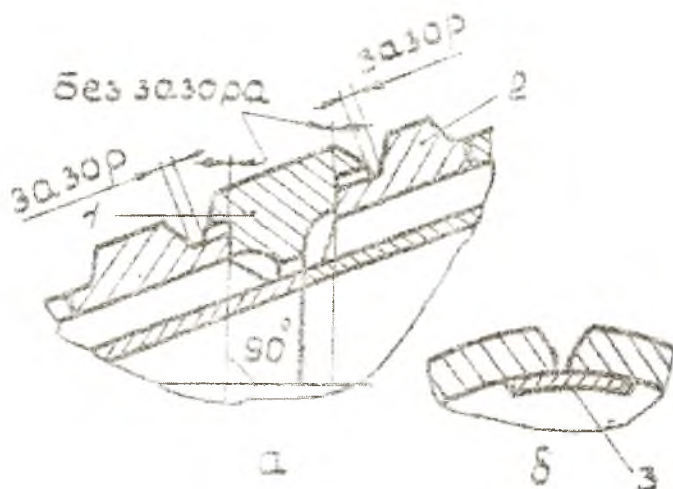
Установка соединительного кольца при сварке секций рубашки корпуса камеры (а) и схема установки подкладки при сварке разъемов этого кольца (б): 1 – разъемное соединительное кольцо; 2 – переходное кольцо рубашки; 3 – подкладка колец (разъемных или сплошных), привариваемых к переходным кольцам
